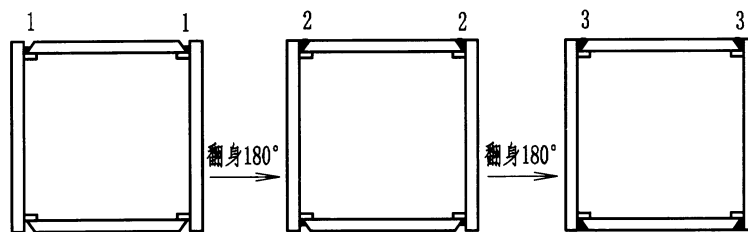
箱形柱腹板与翼缘板角接焊缝的总体焊接顺序
